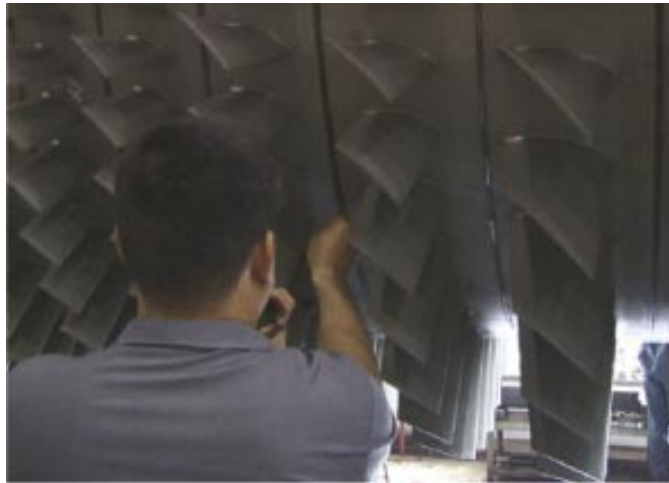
แสดงการ Marks ตำแหน่ง Defects ของ Compressor Blade MS9161E ก่อนเริ่มงาน
